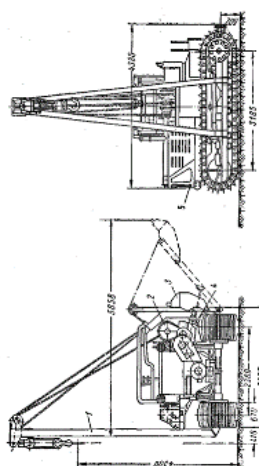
Габаритные размеры крана-трубоукладчика Т-1530В с поворотным противовесом
